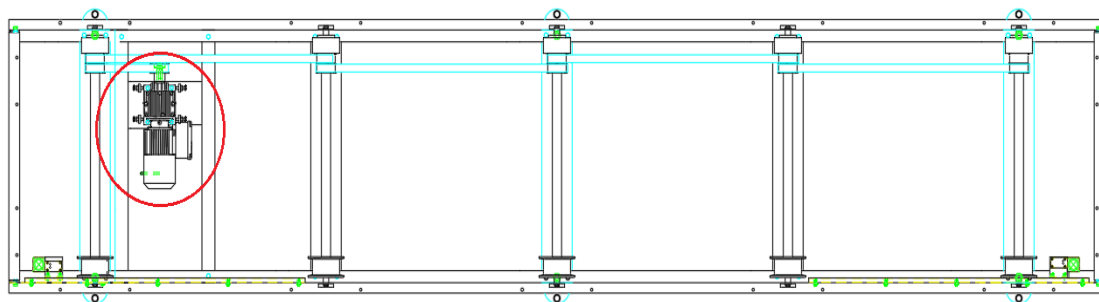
Úprava konstrukce pomocí plexiskla
